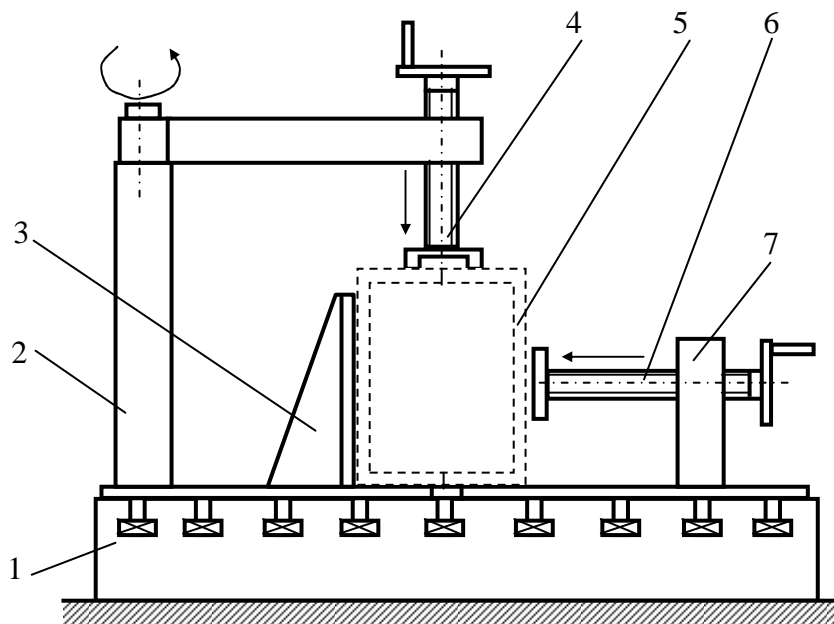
2. Схема компоновки пристрою з комплектів УСП: 1-плита; 2-опора поворотна; 3- упор; 4-вертикальний гвинтовий притискач; 5- виріб; 6-горизонтальний гвинтовий притискач; 7-опора нерухома.
